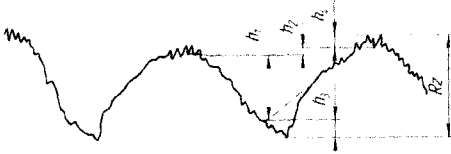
Исходная схема для расчета высоты профиля шероховатости поверхности при механической обработке
